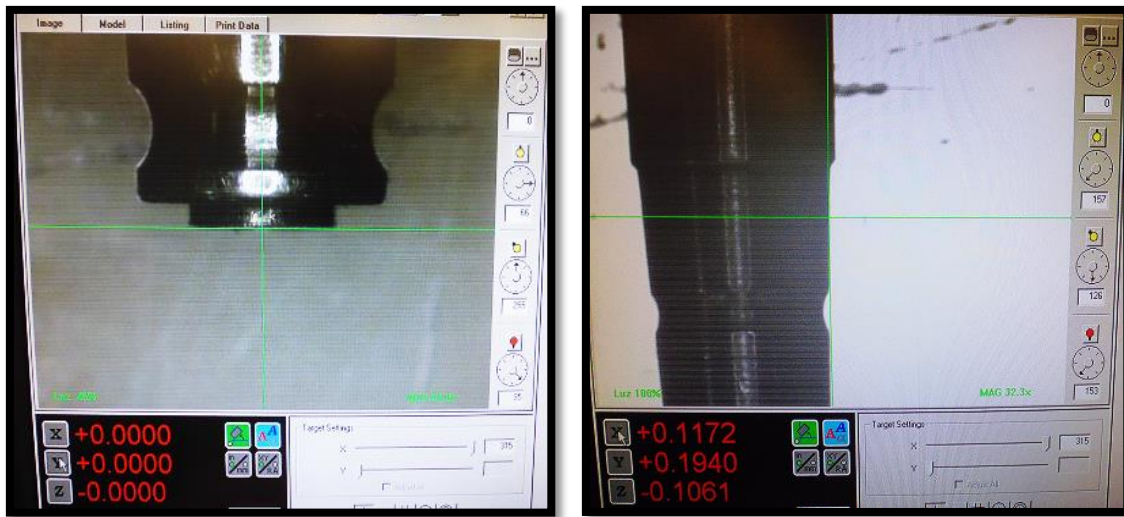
11. Fixture "PIN" utilizado durante el proceso de moldeo de la pieza
